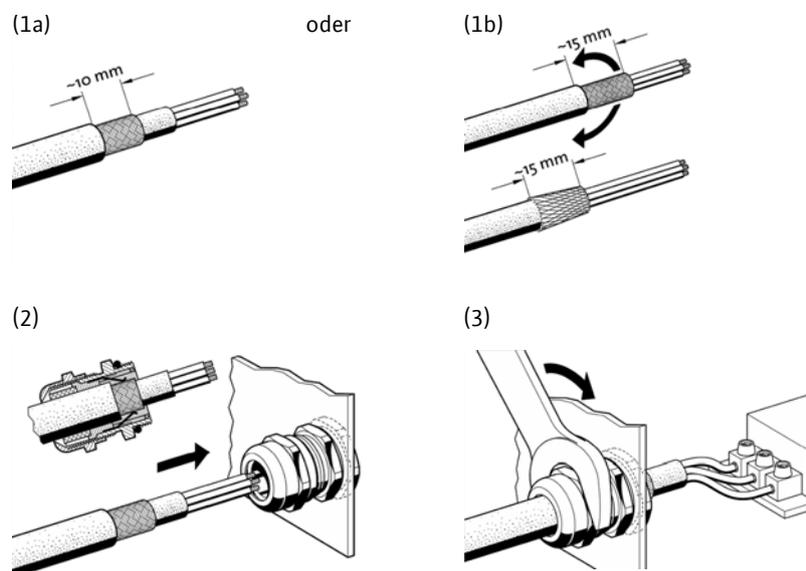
Auflegen von Kabelschirmen auf die EMV-Kabelverschraubungen
